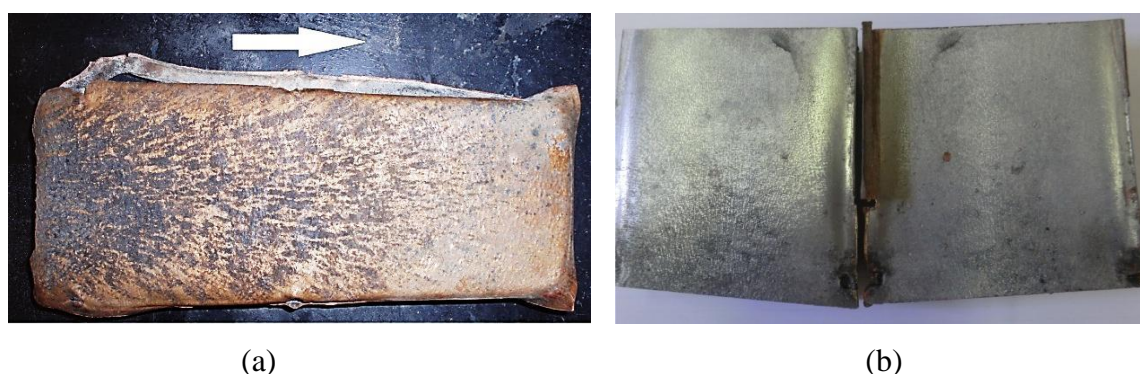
Nova soldadura para *flyer* de 3 mm: (a) rugosidade na superfície da placa de cobre (vista de cima); (b) interface das placas de alumínio, à esquerda e cobre, à direita, do ensaio SE3_N, em que não ocorreu soldadura.
